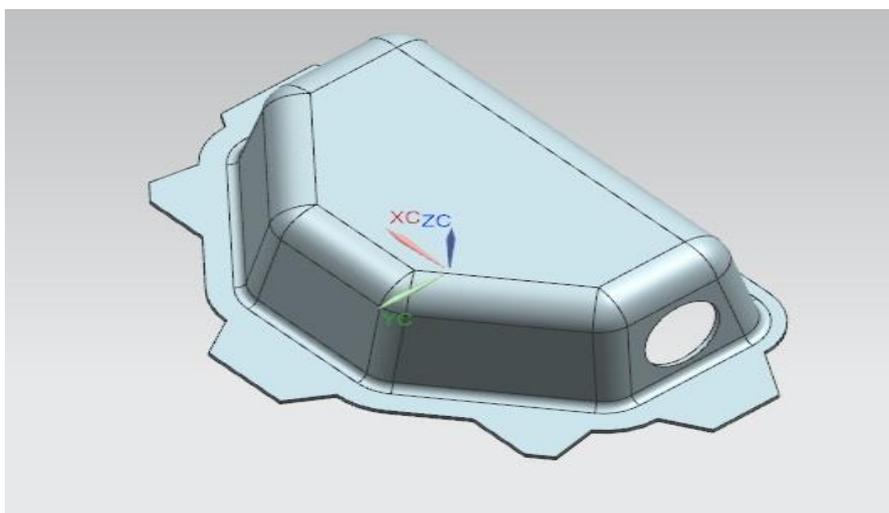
Кожух защитный рычага ручного привода тормоза
